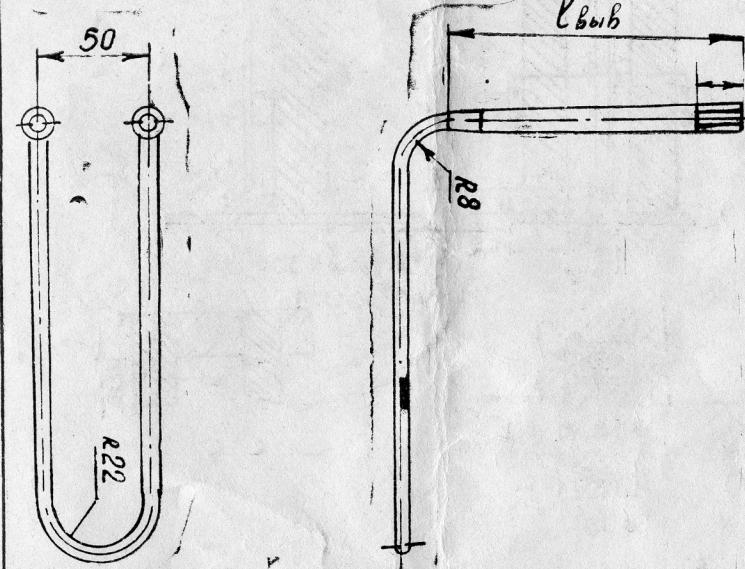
U-образный нагреватель с отогнутыми под 90° выводами.
